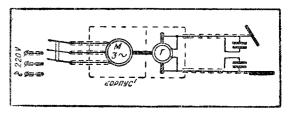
Скема защиты установки для дуговой сварки постоянным током
